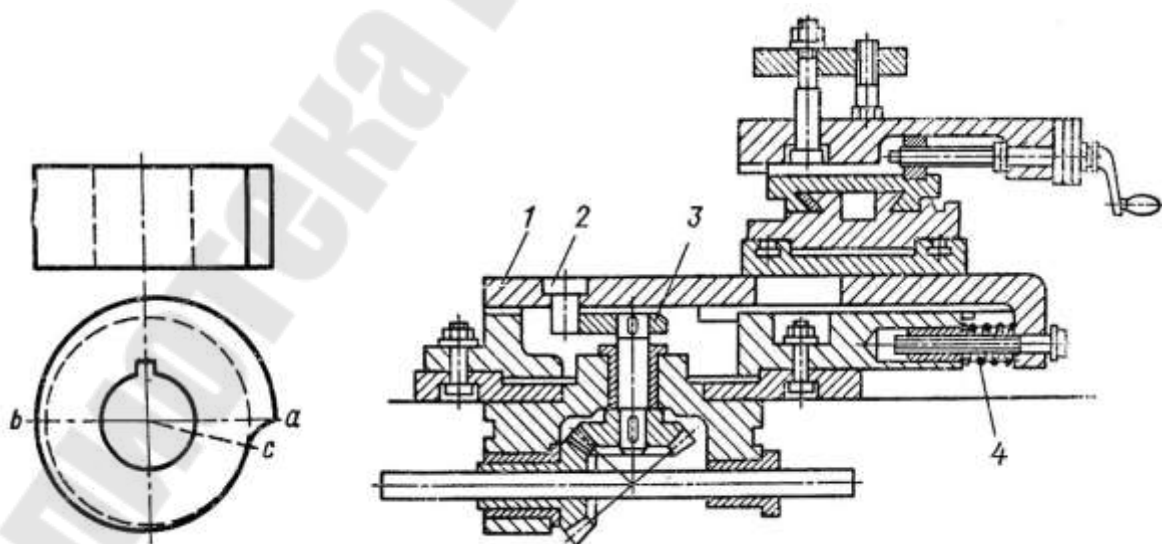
Эскиз сменного кулачка и суппорта токарно-затыловочного станка
